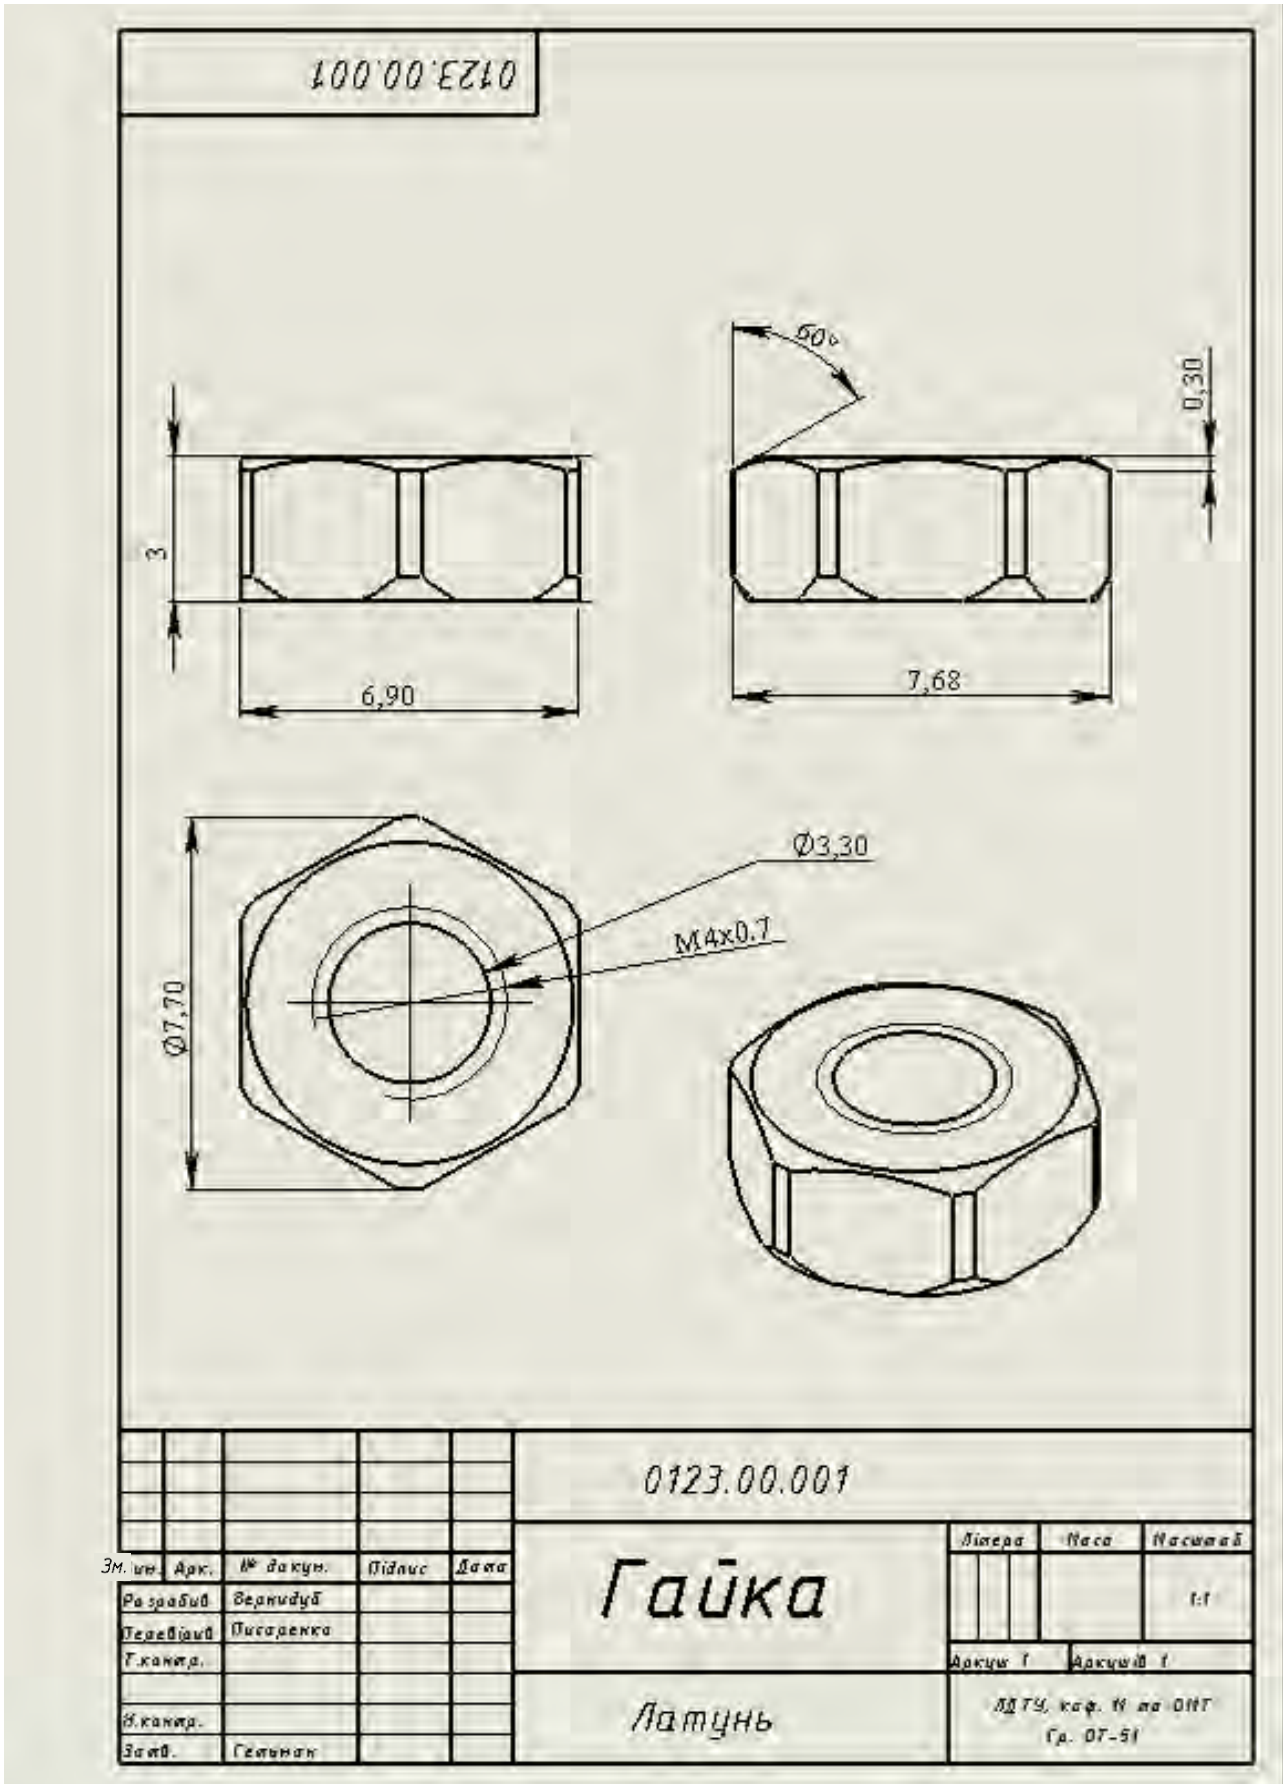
Креслення гайки з основними й допоміжними розмірами
